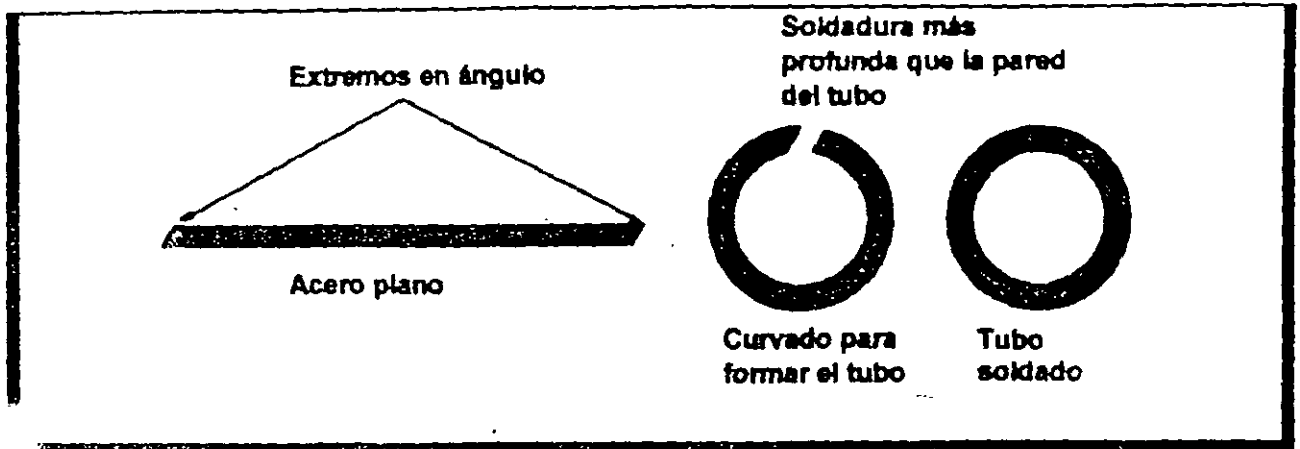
Esquema de fabricación del tubo con soldadura de solapa
